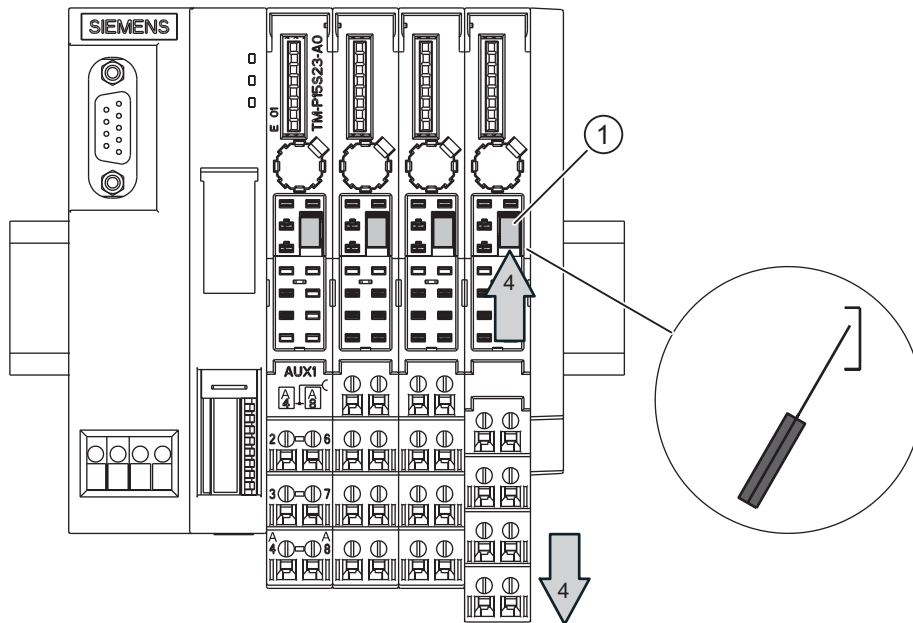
Remplacement de la boîte de bornes sur le module terminal
